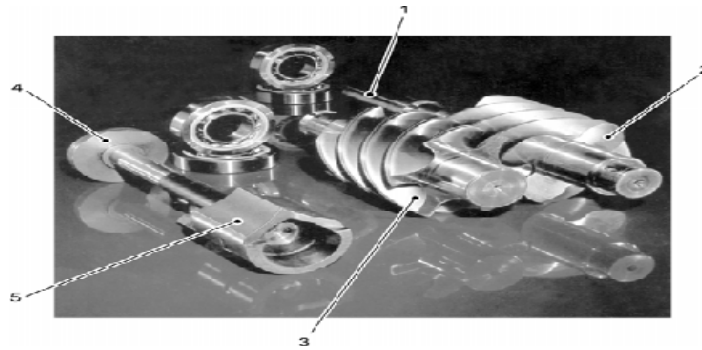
Vue éclatée d'un compresseur à vis birotor [21]
